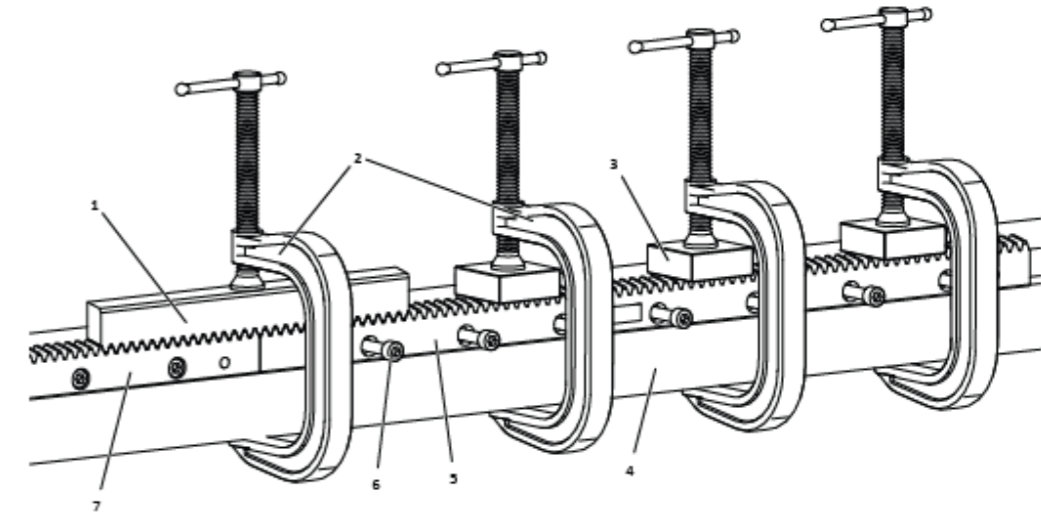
Montage einer weiteren Zahnstange (Beispiel)
